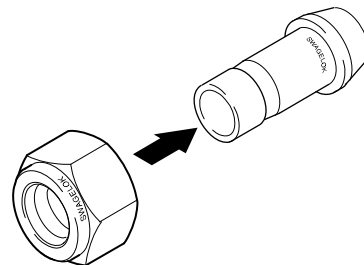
Coloque la tuerca sobre el extremo de férula mecanizada del conector de puerto
